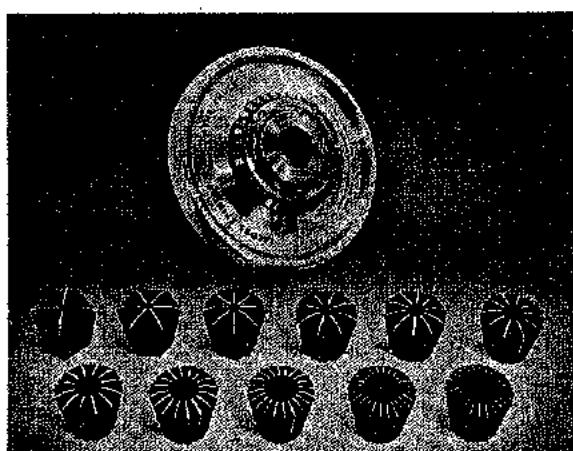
Plato "Jacobs" de fijación al extremo del husillo y casquillos flexibles de caucho (Monarch Machine Tool Co.).
